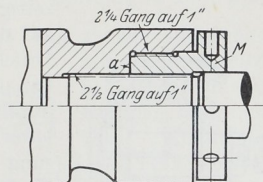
Befestigung der Stange durch Differentialgewinde.
